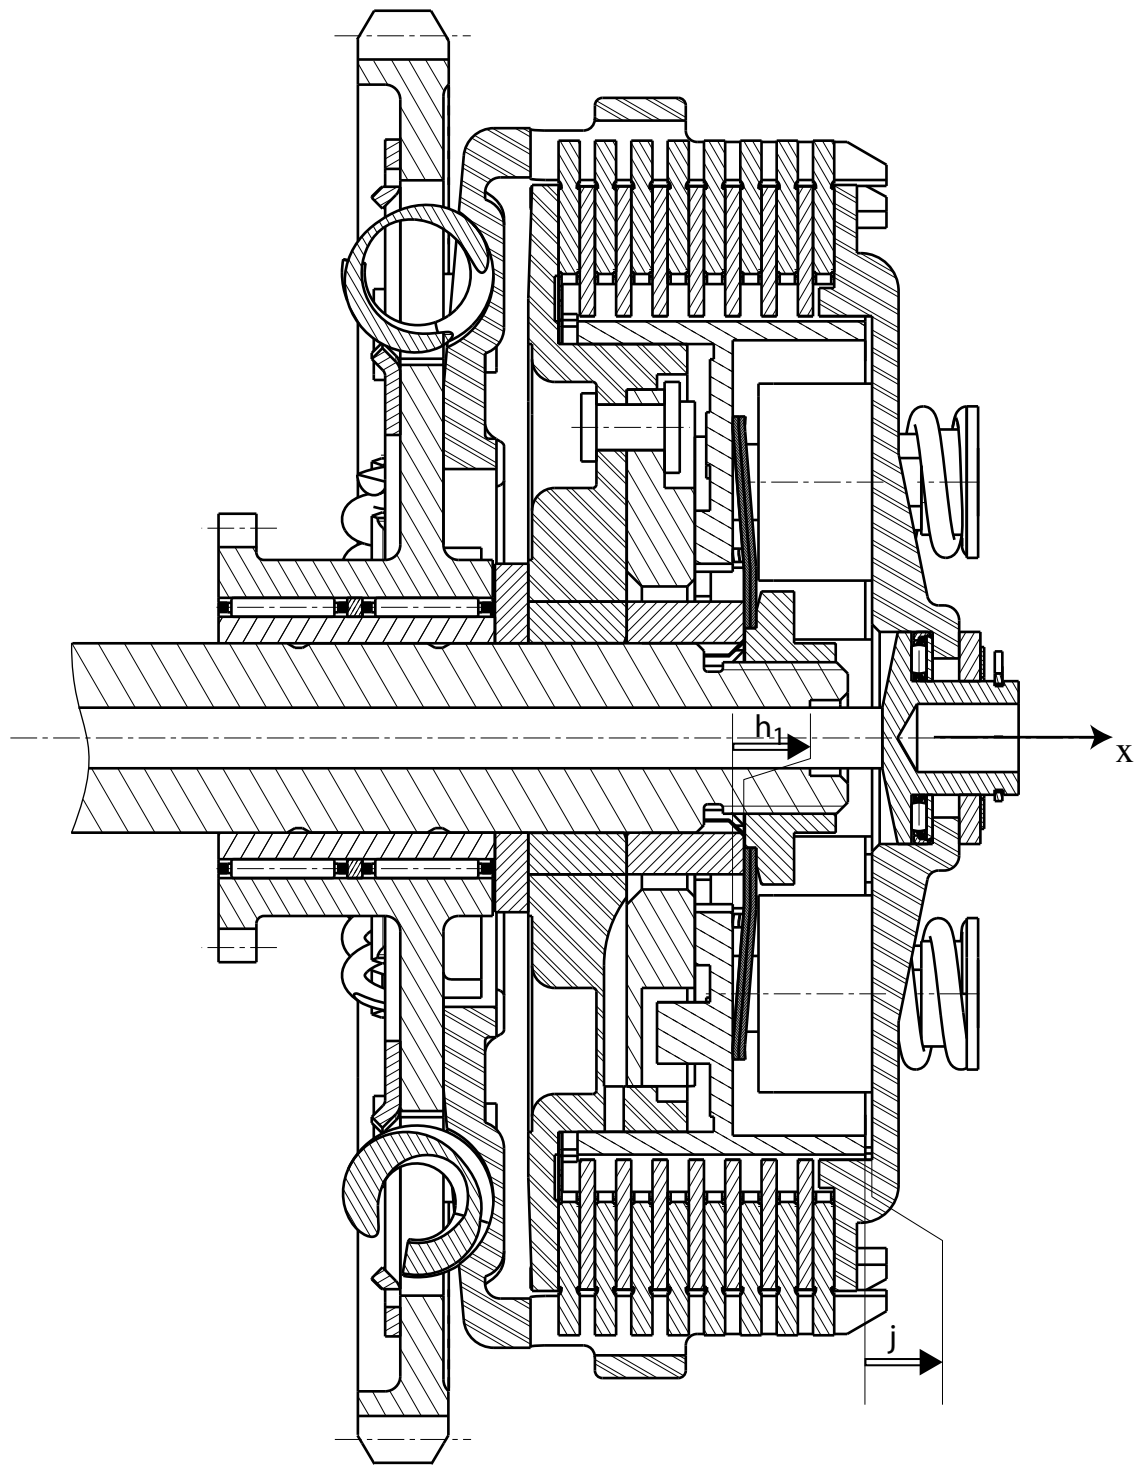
Vue d'ensemble de l'embrayage « sliding-clutch »
